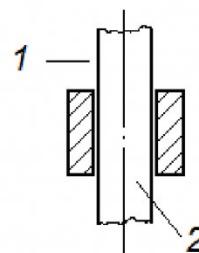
Универсальный направляющий элемент (группа II): 1 - подвижная часть (относительно корпуса); 2 – неподвижная часть.
